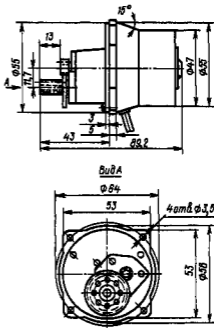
Габаритные и установочные размеры двигателя ГР-206
